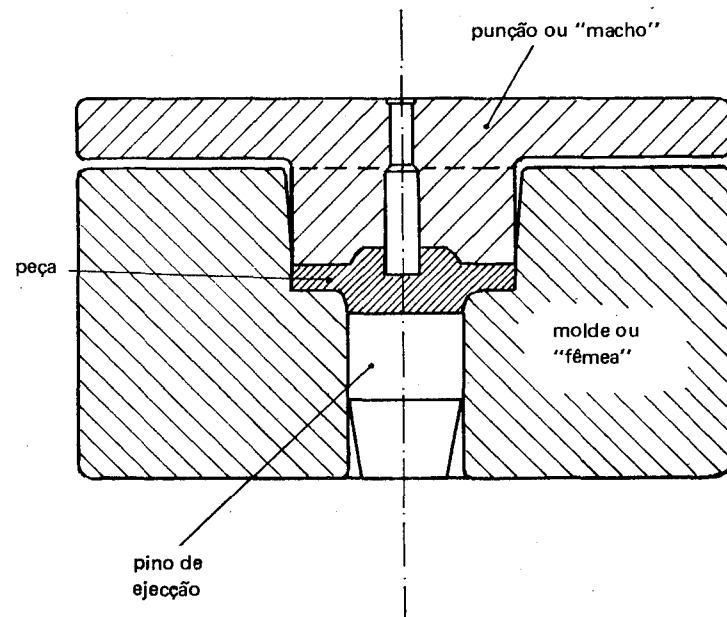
Tipo de molde para moldagem de plástico por compressão.
